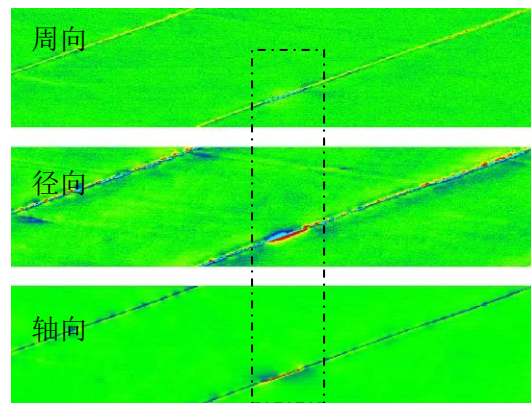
螺旋焊缝缺陷的三轴漏磁信号
